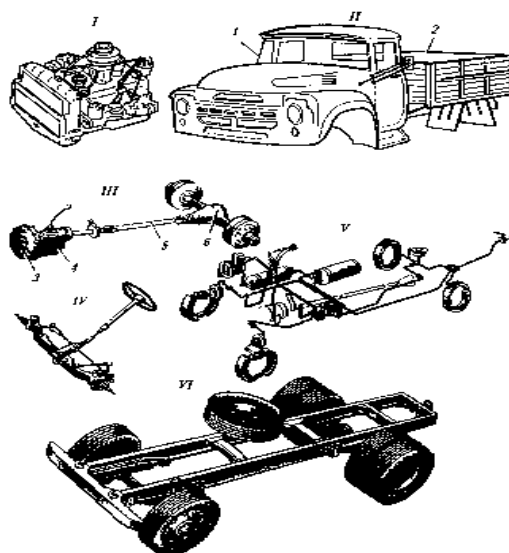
Основные части автомобиля ЗИЛ-130: I—двигатель; II—кузов; III—трансмиссия; IV— рулевое управление; V—тормозная система; VI— ходовая часть; 1 — кабина; 2— грузовая платформа; 3— сцепление; 4 — коробка передач; 5— карданная передача; 6— главная передача (ведущий мост)
